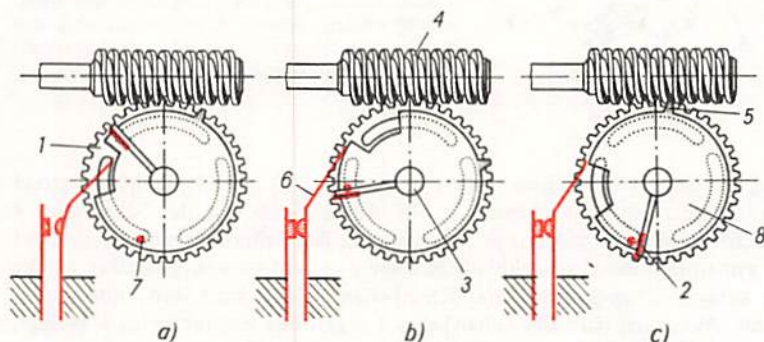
Kontaktsteuerung für eine elektrische Uhr
